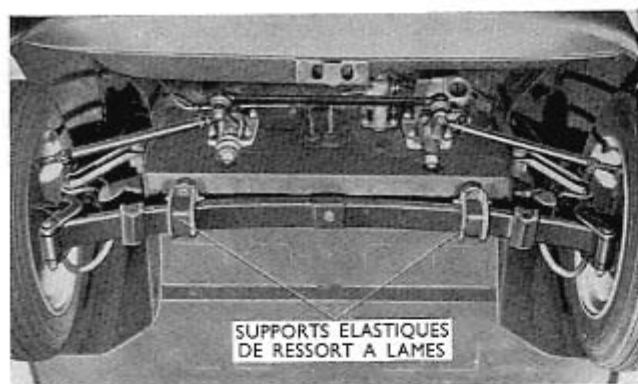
Partie avant de la voiture, vue d'en bas.
